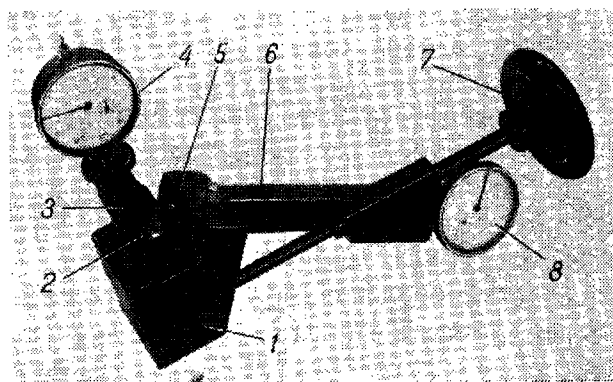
Приспособление для проверки суммарной жесткости токарно-винторезного станка
